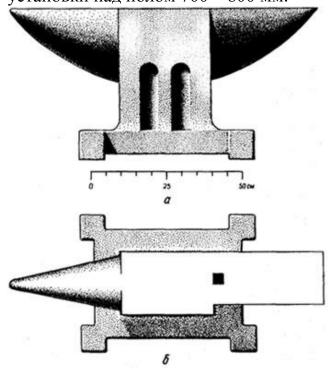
Двурогая наковальня: а - вид сбоку; б - вид сверху
